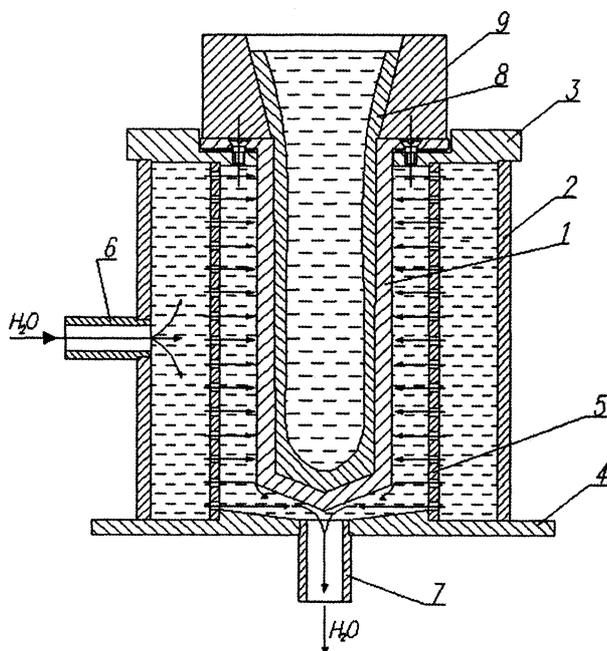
Схема литья в кристаллизатор со струйной системой охлаждения: 1 – стакан; 2 – корпус; 3 – верхний фланец; 4 – нижний фланец; 5 – экран; 6 – подводящий патрубок; 7 – отводящий патрубок; 8 – отливка; 9 – захват
